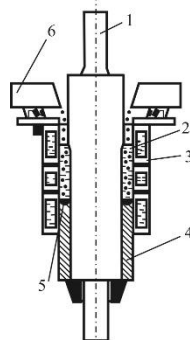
Схема электрошлаковой наплавки зернистой присадкой в токоподводящем кристаллизаторе
